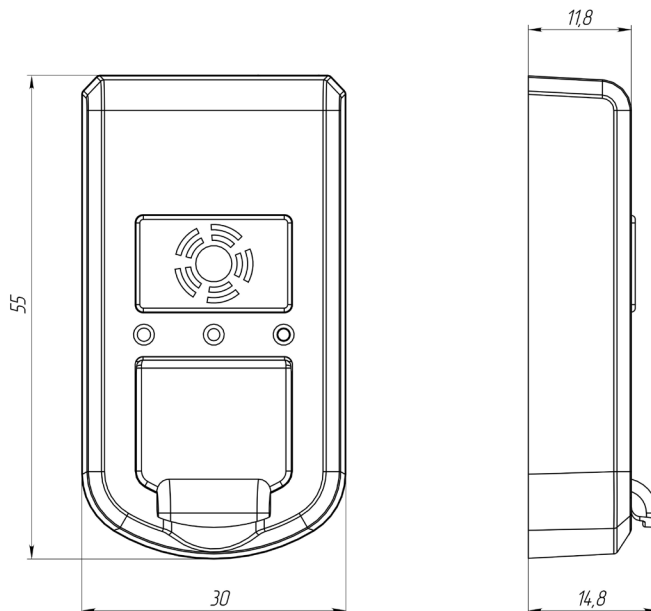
Габаритный чертёж БИП-К УВЭОС
